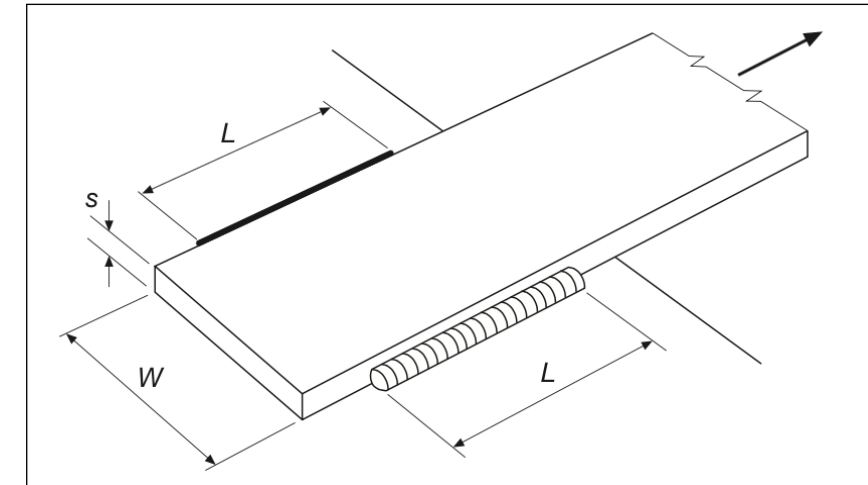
r. Esquema soldadura. Fuente: EAE.
